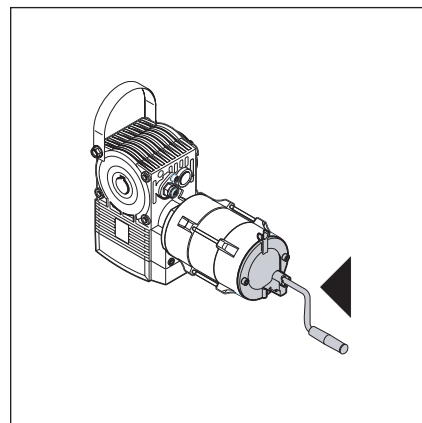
Фланцевый привод с рукояткой для аварийного открывания ворот
